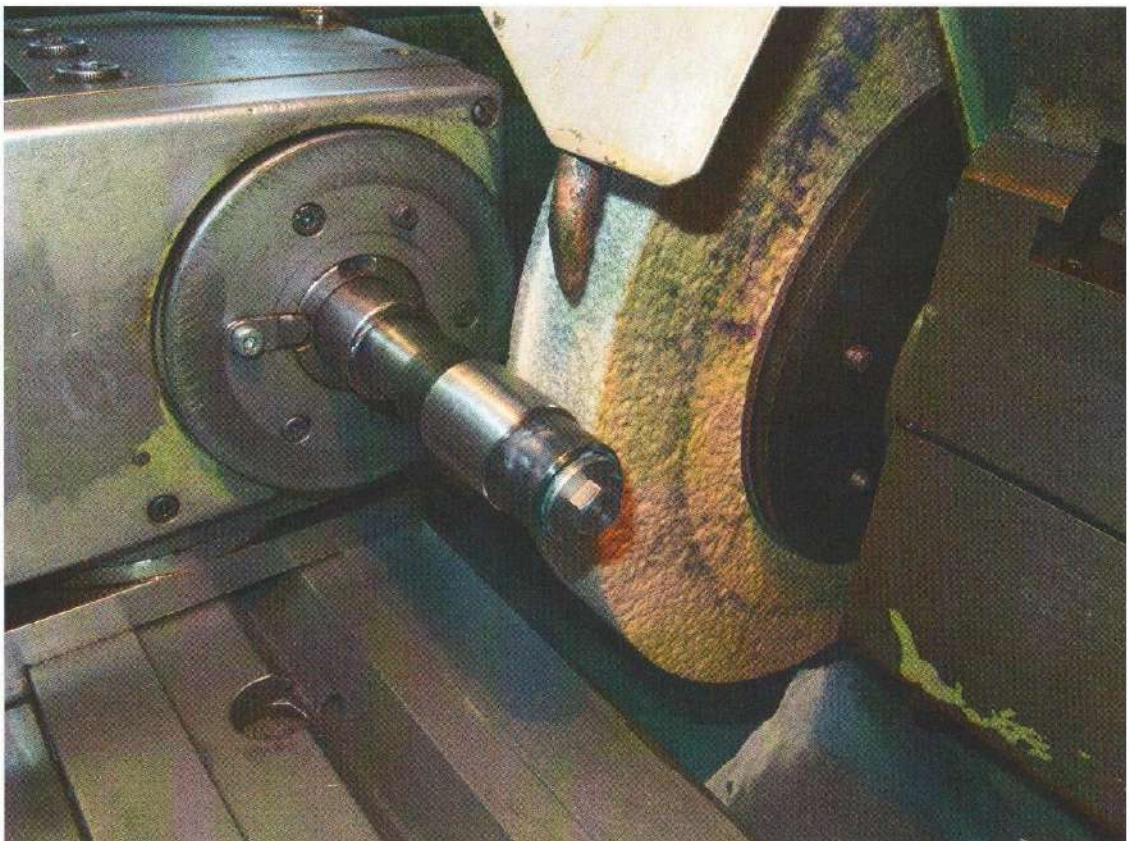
Процесс шлифования закрепленной на оправке заготовки
